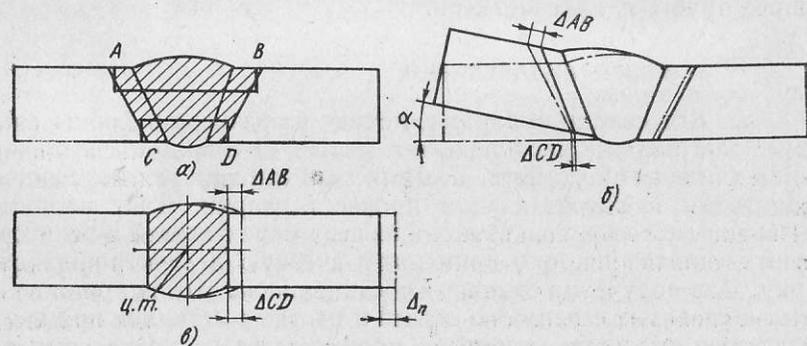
Схема образования внешних сварочных деформаций
